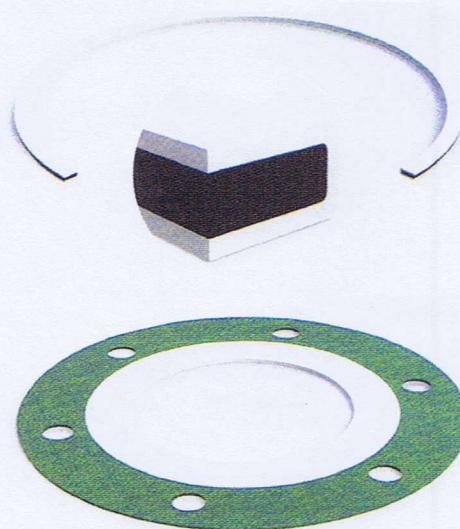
Комбинированные уплотнения паронит-фторопласт для герметизации мест установки трубопроводной арматуры
